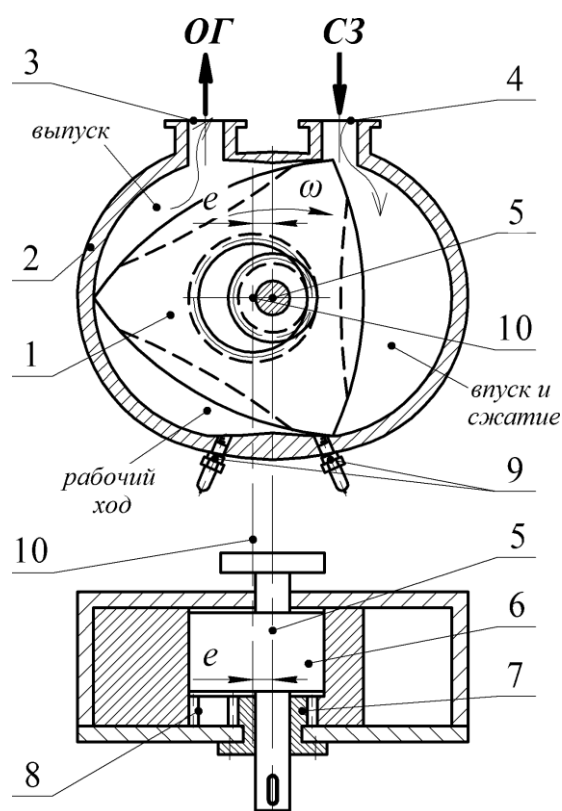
Принципиальная схема роторного (роторно-поршневого) двигателя Ванкеля:
